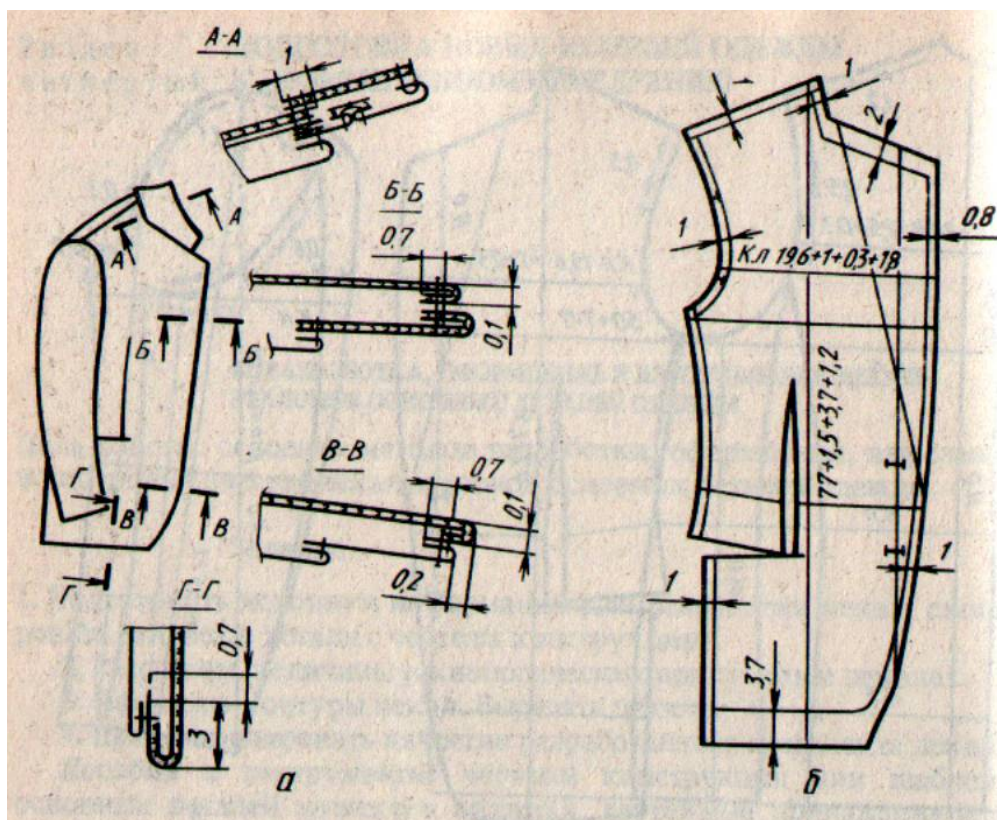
Сборочный чертеж (а) и схеме конструкции лекала полочки (б) мужского пиджака
